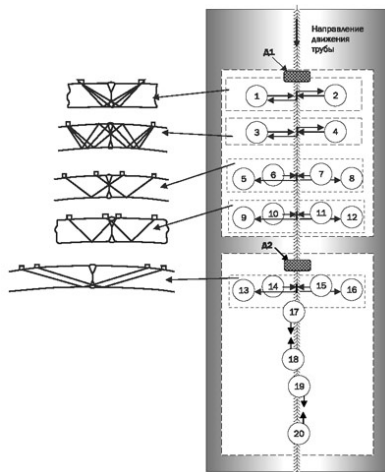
Схема расположения акустических головок при контроле продольных сварных соединений:
